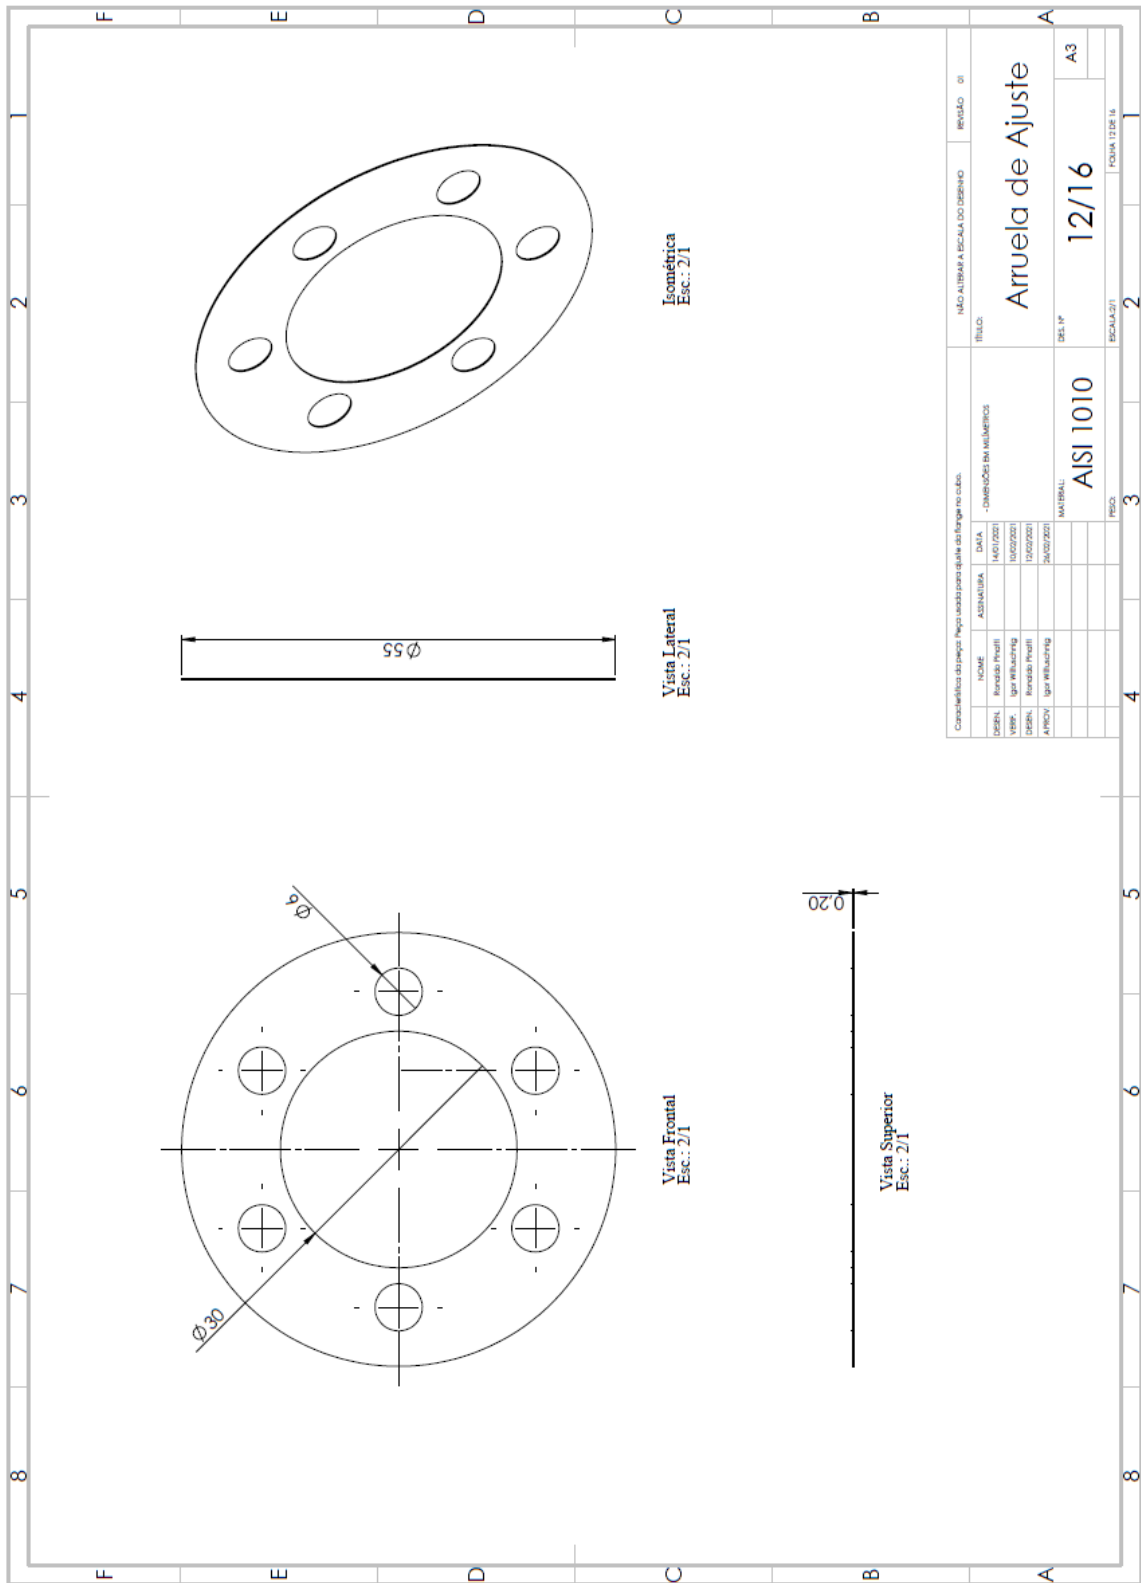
Desenho técnico do anel modular que cobre os segmentos do rotor.
